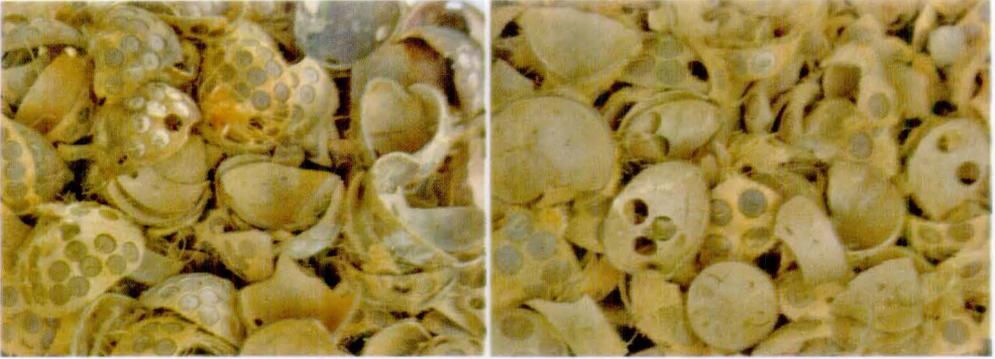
Bathok yang sudah di-*ngeplong* bentuk kancing baju berbagai ukuran.
